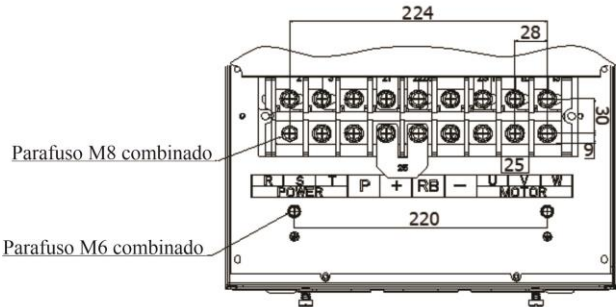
Terminal circuito principal 75kW G3B (Chassis No.: A19)
